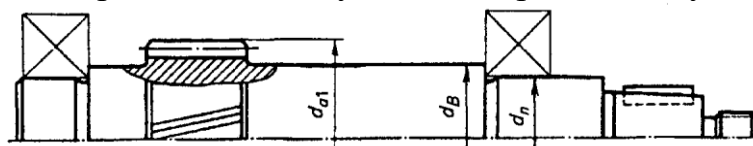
Вал-шестерня цилиндрической косозубой передачи
